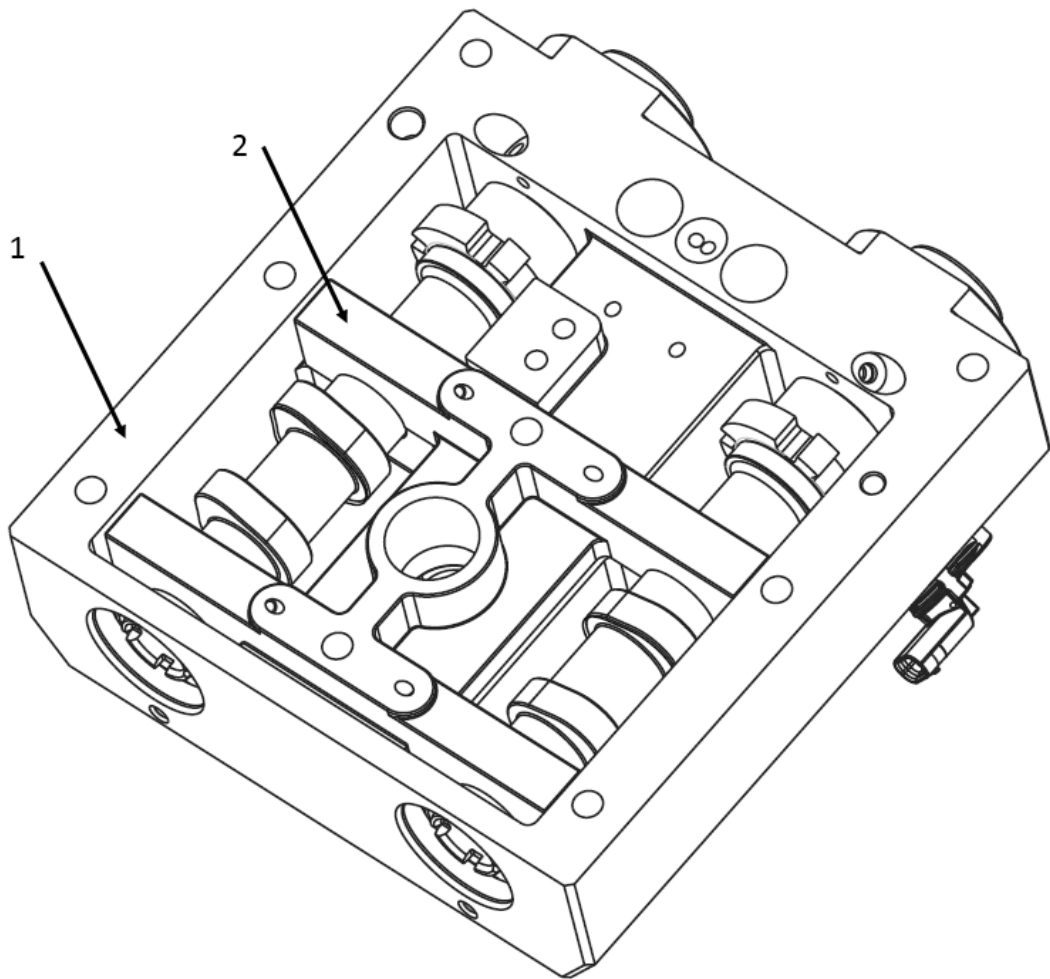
Víko hlavy válce, varianta 2 – pohled shora
